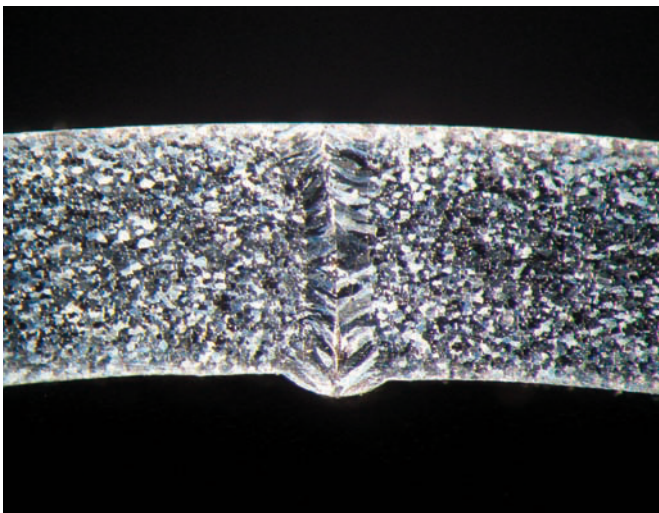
Makroaufnahme, schmale Laserschweißnaht 1.4521 in der Übersicht
